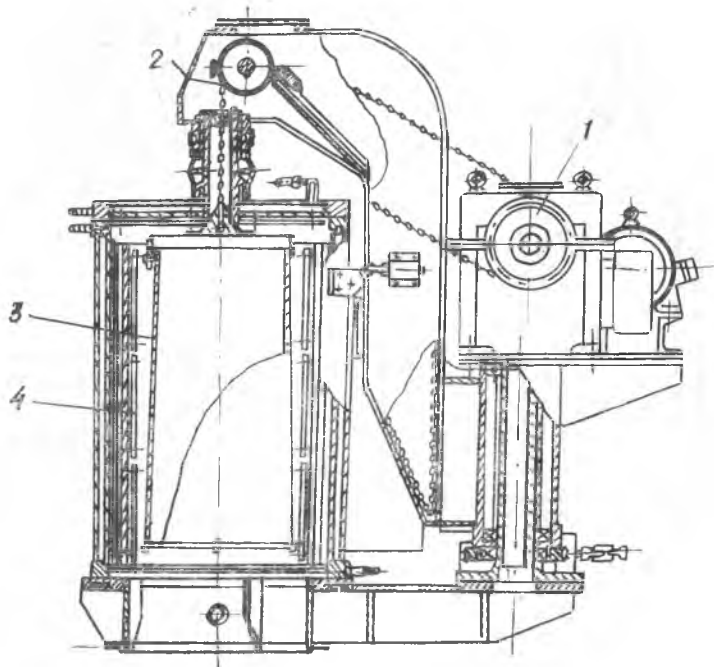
Камера загрузки печи ОКБ-571 Б: 1 — привод; 2 — барабан; 3 — загрузочная корзинка; 4 — нагреватели
